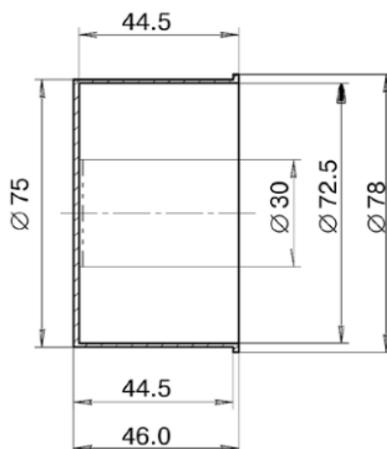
Стакан металлический для поверки поверхностных зондов
